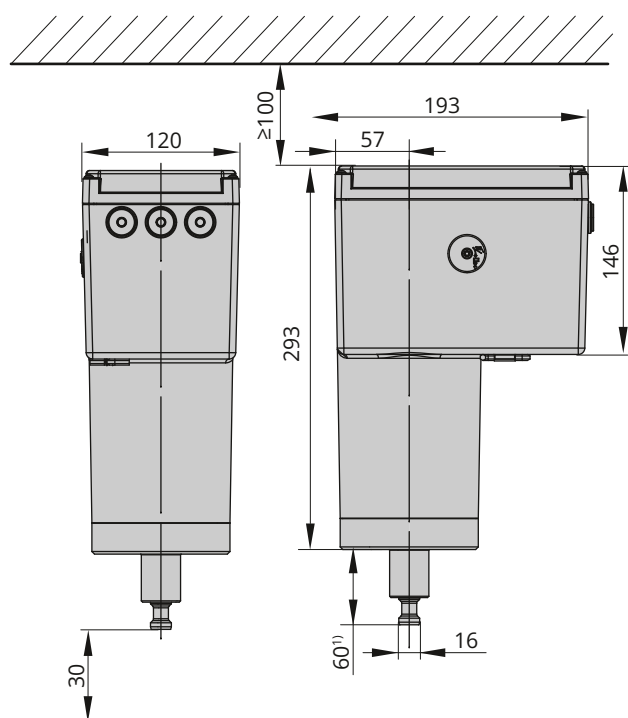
Dimensions en mm · Type 3374-35, exécution Forme A
